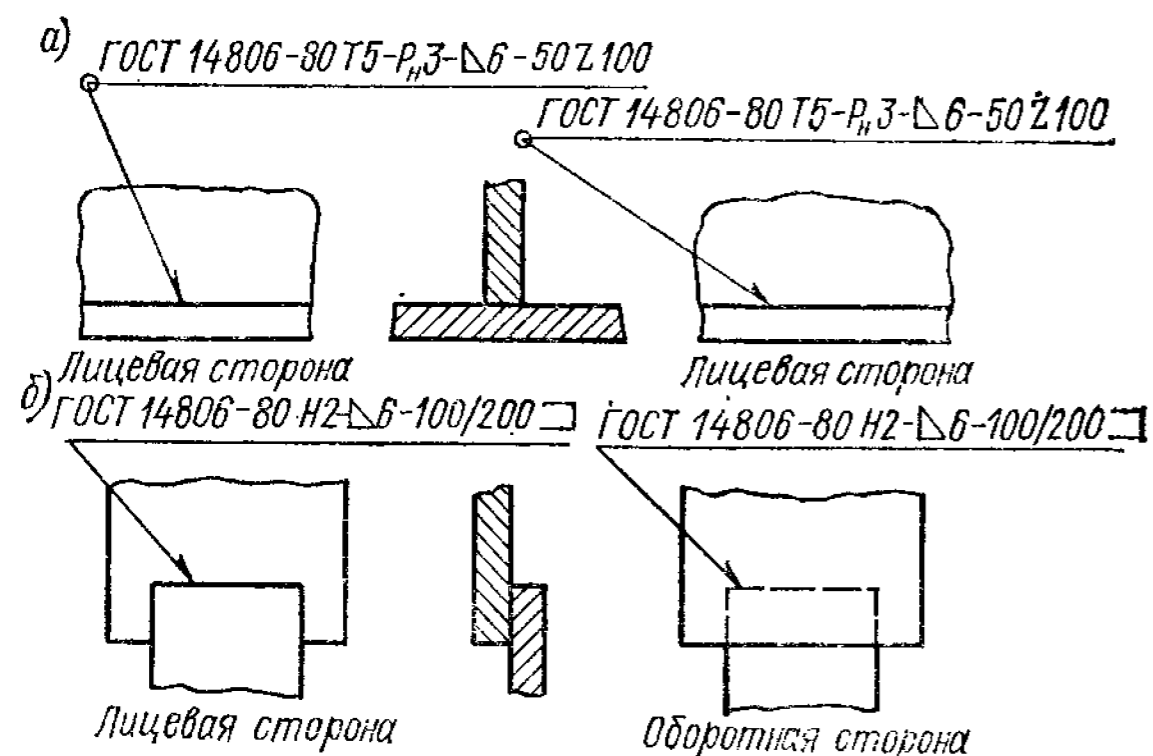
Примеры условного обозначения на чертежах сварных швов
